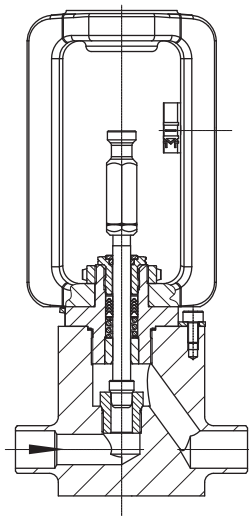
· Vanne haute pression type 3252 à passage droit avec embouts à souder
